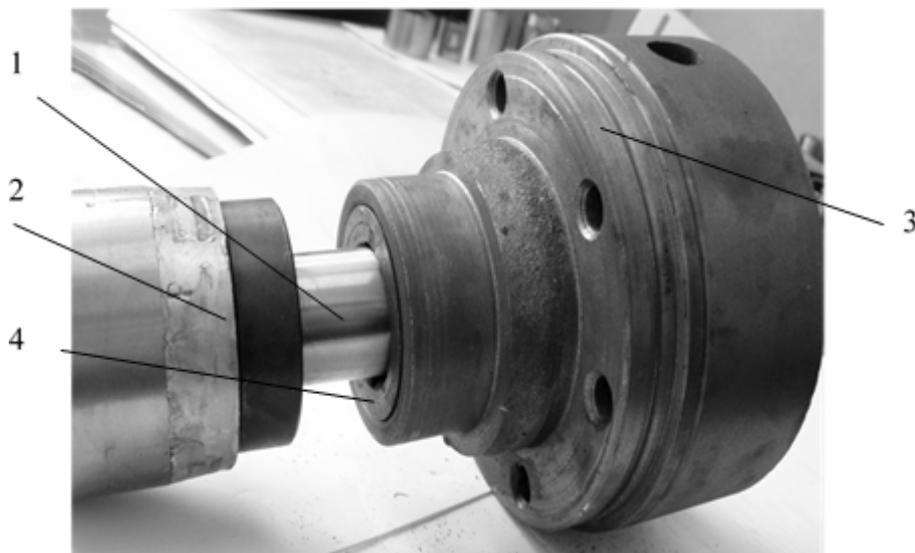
Фотографии части электродвигателя: 1 — ротор; 2 — статор; 3 — щит подшипниковый; 4 — подшипник
